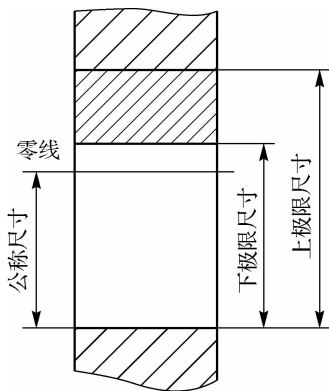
公称尺寸、上极限尺寸和下极限尺寸
